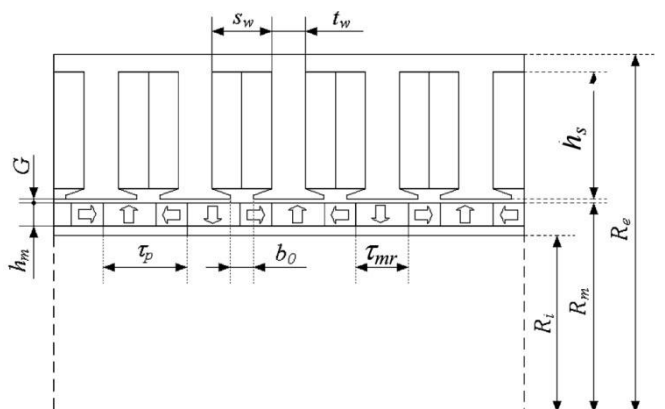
Основные конструктивные параметры цилиндрической ПМ-машины.
